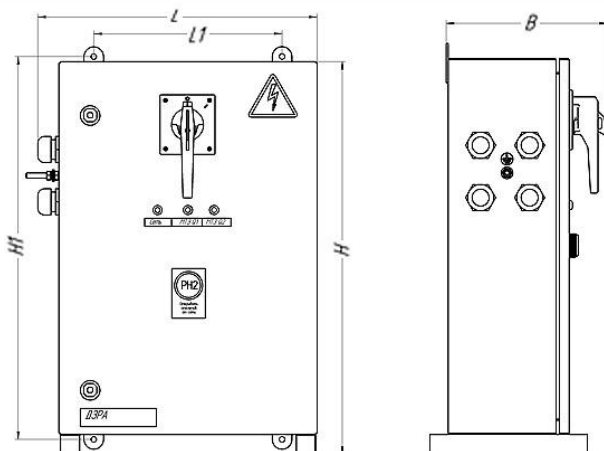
Общий вид, габаритные и установочные размеры АОШ-Х-Х-127В/220В (1,6-10 кВА) мобильного
